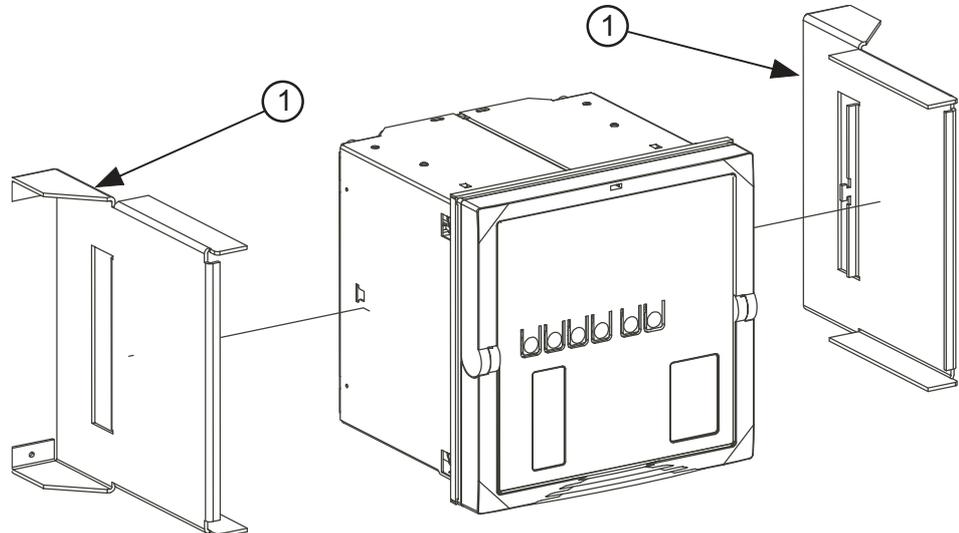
1 Montaje del relé y el marco metálico para la llave de ensayo RTXP 18
